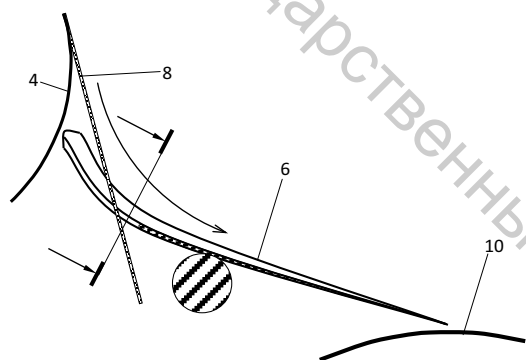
Схема расположения средства для направления кожевенного полуфабриката между транспортером и рабочими валами, вид с боку, по разрезу А-А из рис.1,б
